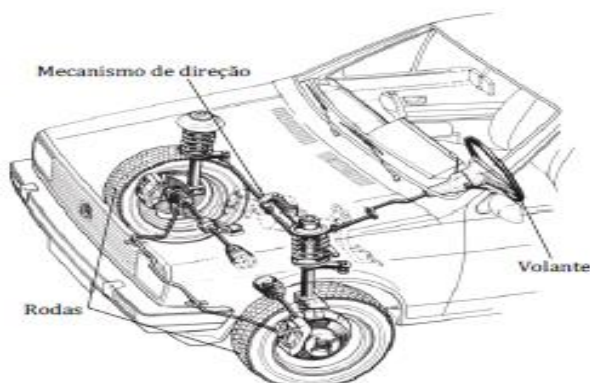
Partes constituintes de um mecanismo de direção [4].
